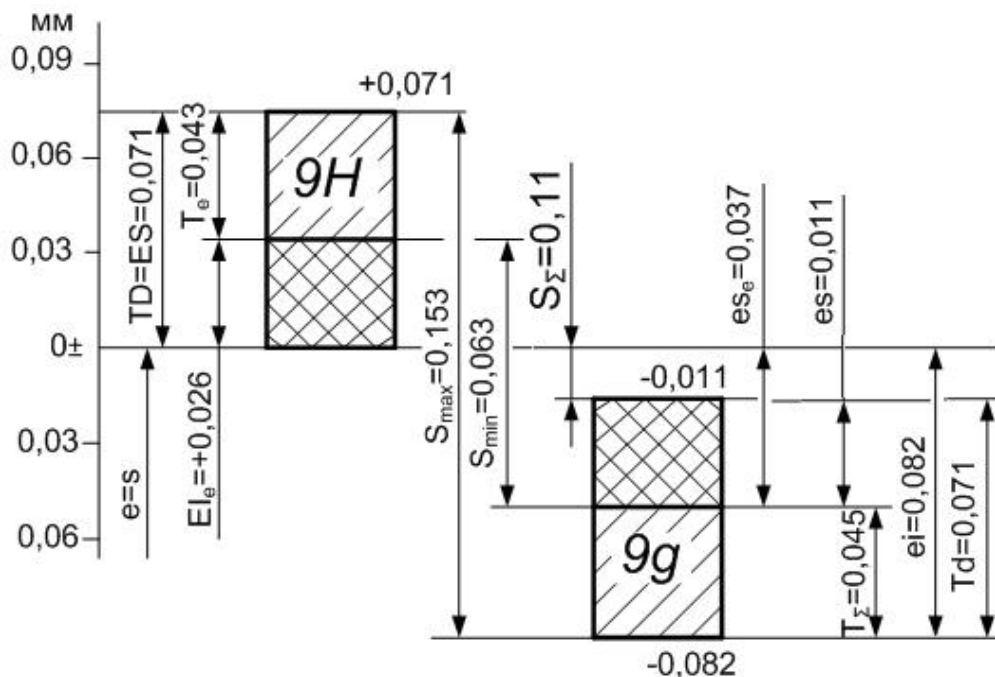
Схема розташування полів допусків за бічними поверхнями зубів:
